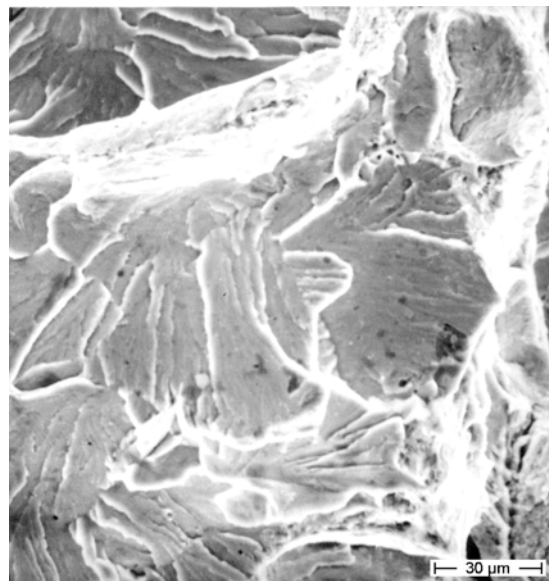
einzelne Spaltflächen (Ausschnitt aus Bild 4)
